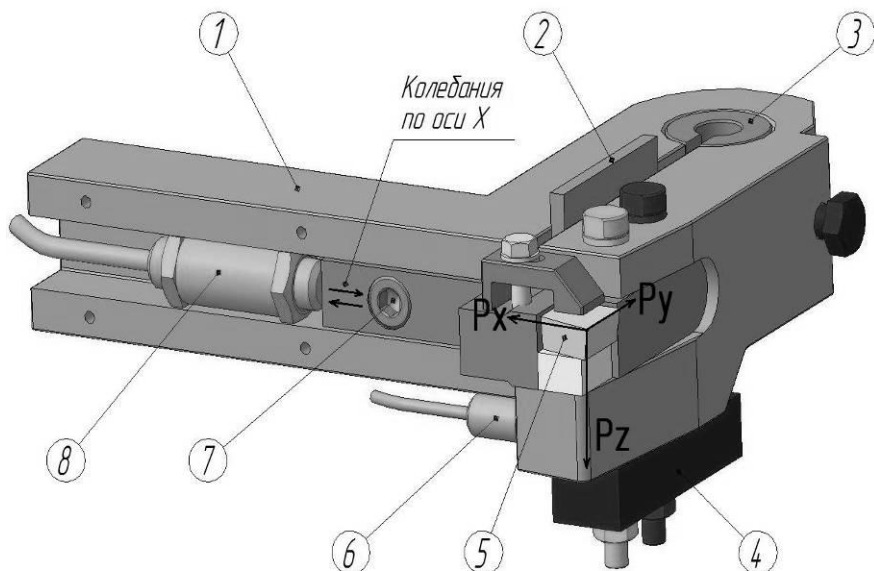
Конструкция устройства для изучения регенеративных колебаний при точении: 1 – упругая державка режущей пластины; 2 – вязкоупругая среда (демпфер); 3 – разрезная втулка (изменение жесткости); 4 – дополнительная масса; 5 – режущая пластина; 6 – акселерометр; 7 – болт жесткой фиксации УСР (по оси X); 8 – бесконтактный токовихревой датчик перемещений
